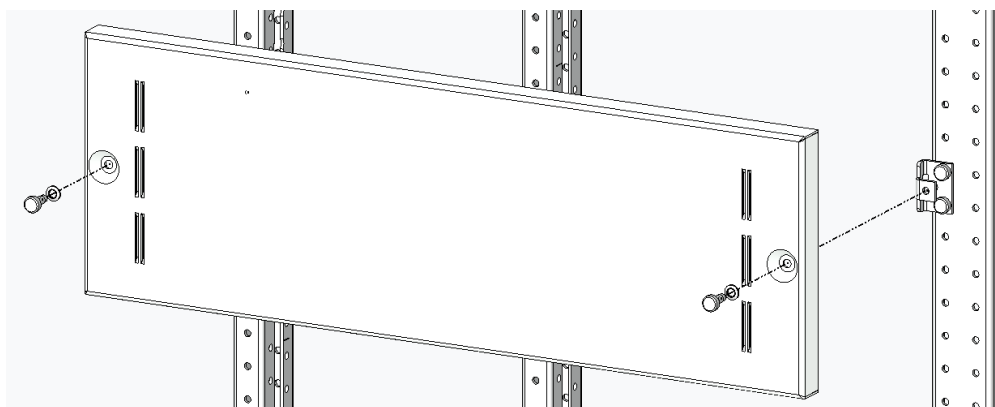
/ Fig. 24 Montagem de coberturas cegas / Fixation of blanking cover
